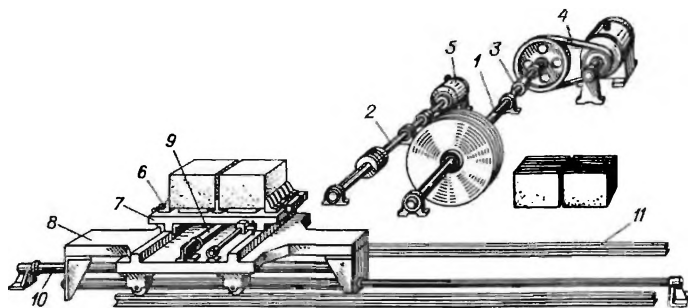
Кинематическая схема распиловочного многодискового одновального станка модели СМР-004
